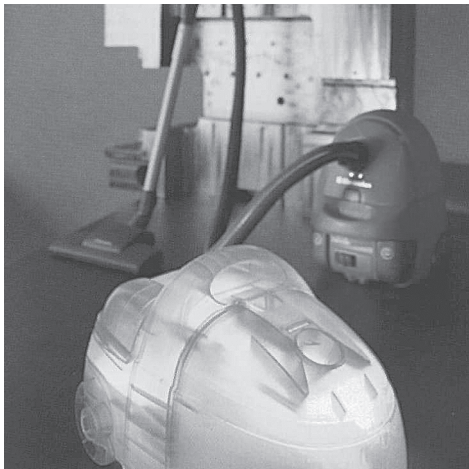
Pièce réalisée sur machine 3D systems : prototype de forme de la carrosserie d'un aspirateur.
